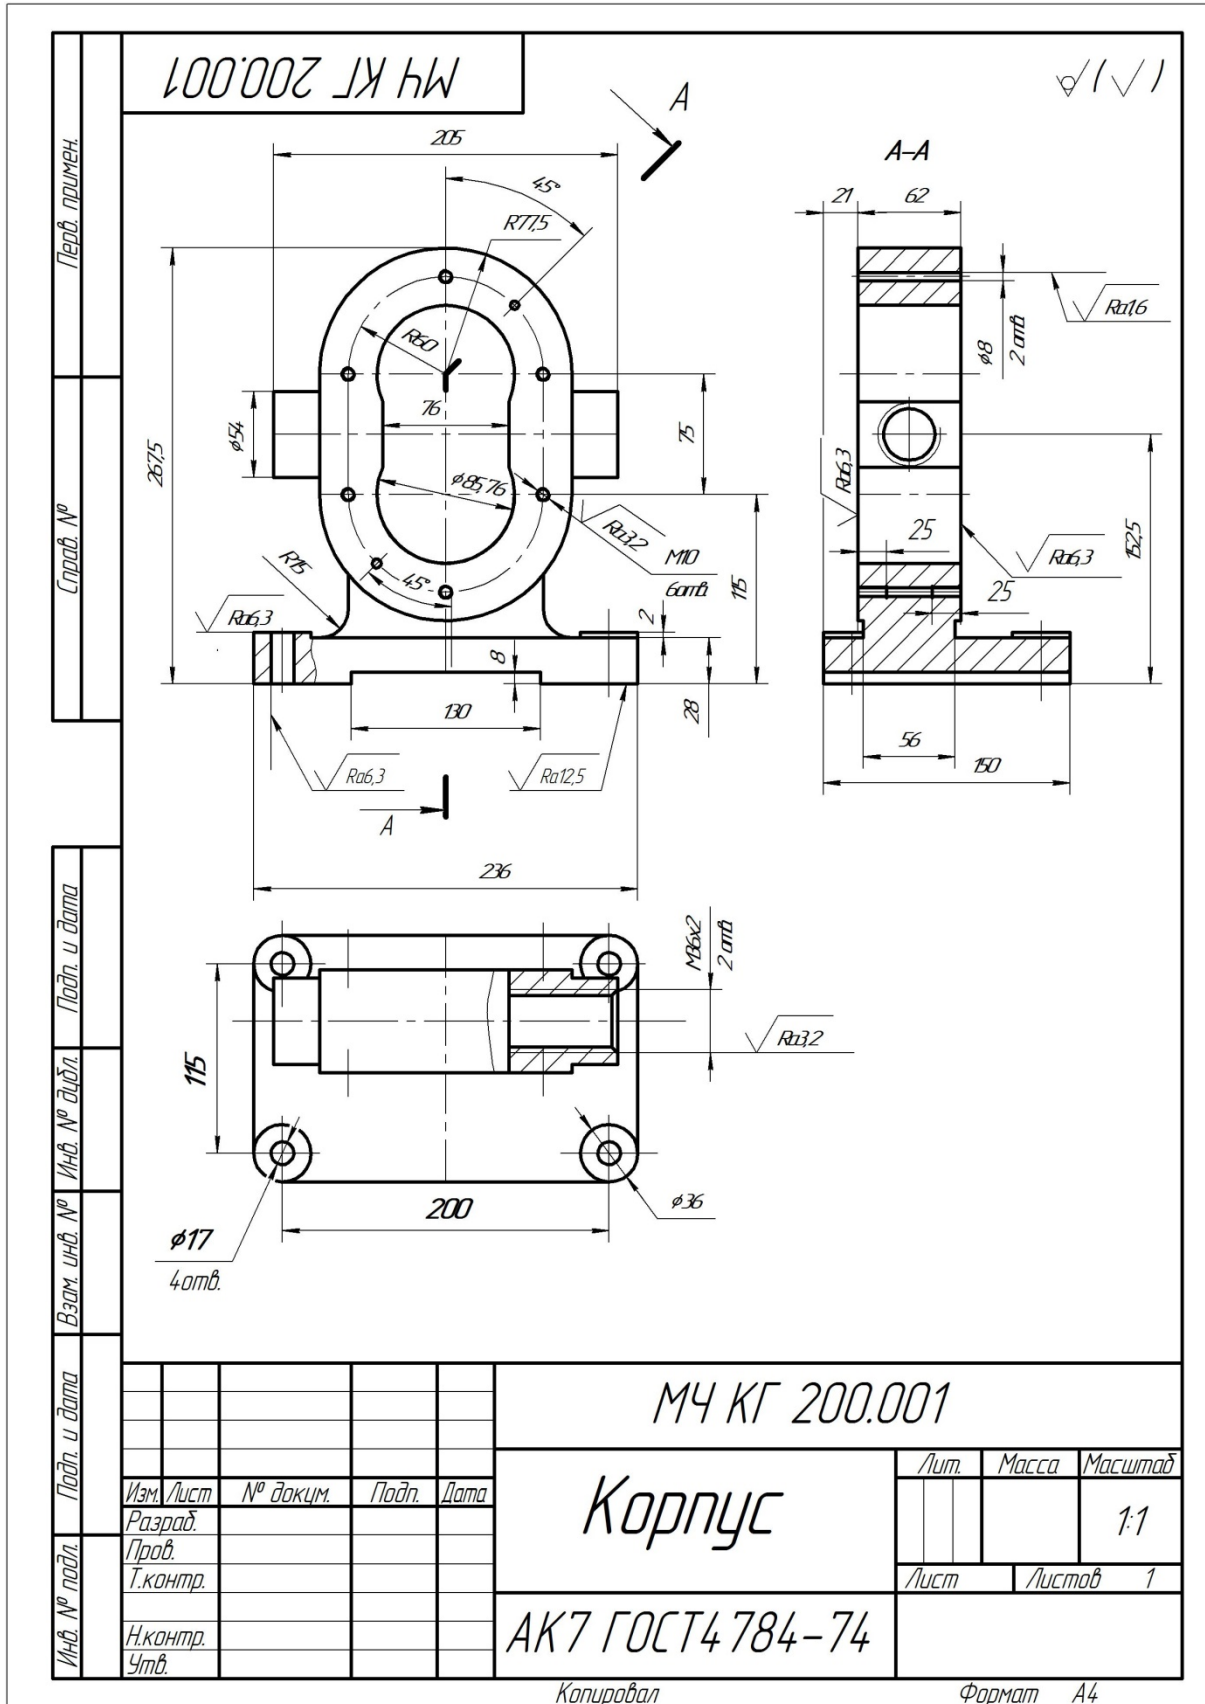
Рабочий чертеж «Корпуса», поз.1.
